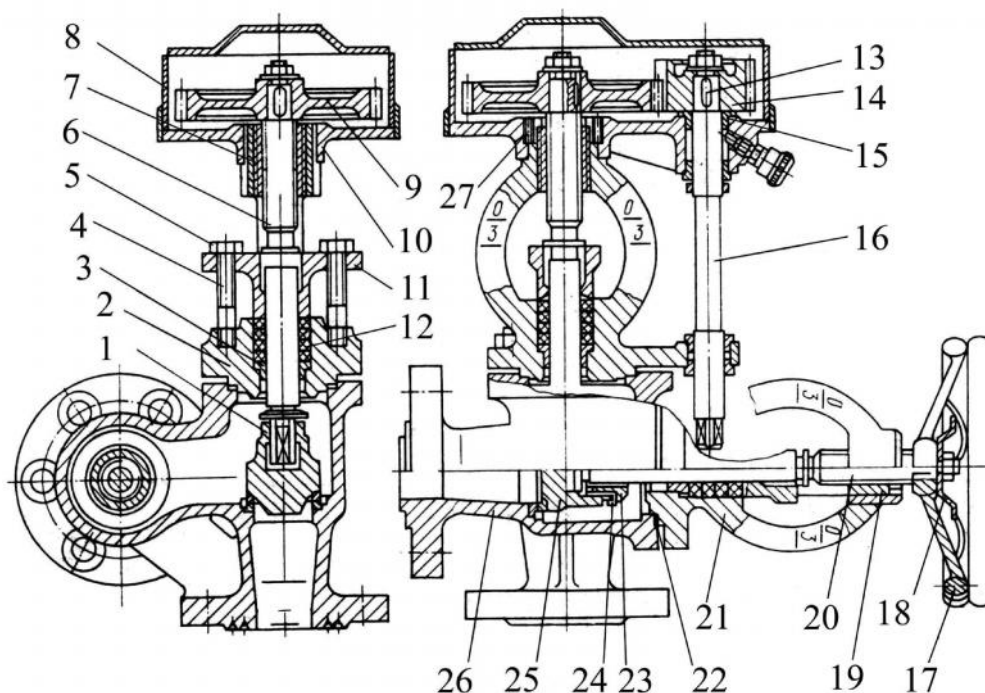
Двойной питательный клапан: 1, 25 – тарелка; 2, 21 – крышка; 3 – втулка (грундбукса); 4 – шпилька; 5 – гайка; 6, 20 – шпиндель; 7, 19 – нарезная втулка; 8 – кожух; 9, 14 – зубчатое колесо; 10 – кронштейн; 11 – нажимная втулка; 12 – сальниковое уплотнение; 13 – шпонка; 15 – втулка; 16 – валик; 17 – маховик; 18 – шайба; 22 – прокладка; 23 – колпачок; 24 – шайба; 26 – корпус; 27 – винт
